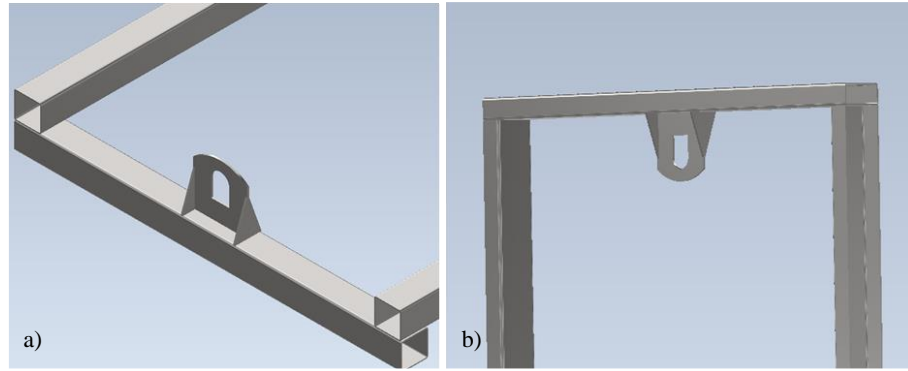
oreja de anclaje para levante. a) sobre el marco pivotante donde descansa la rueda. b) bajo el marco de la estructura principal donde reposa el peso de la estructura.
